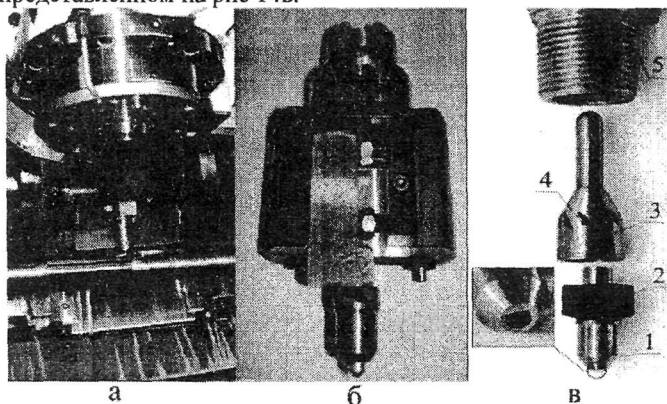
Отделочное выглаживание шпинделя задвижки на токарно-фрезерном центре MULTUS B-300W (а); быстросменный выглаживатель в инструментальной оправке центра (б); узел динамической стабилизации (в)
